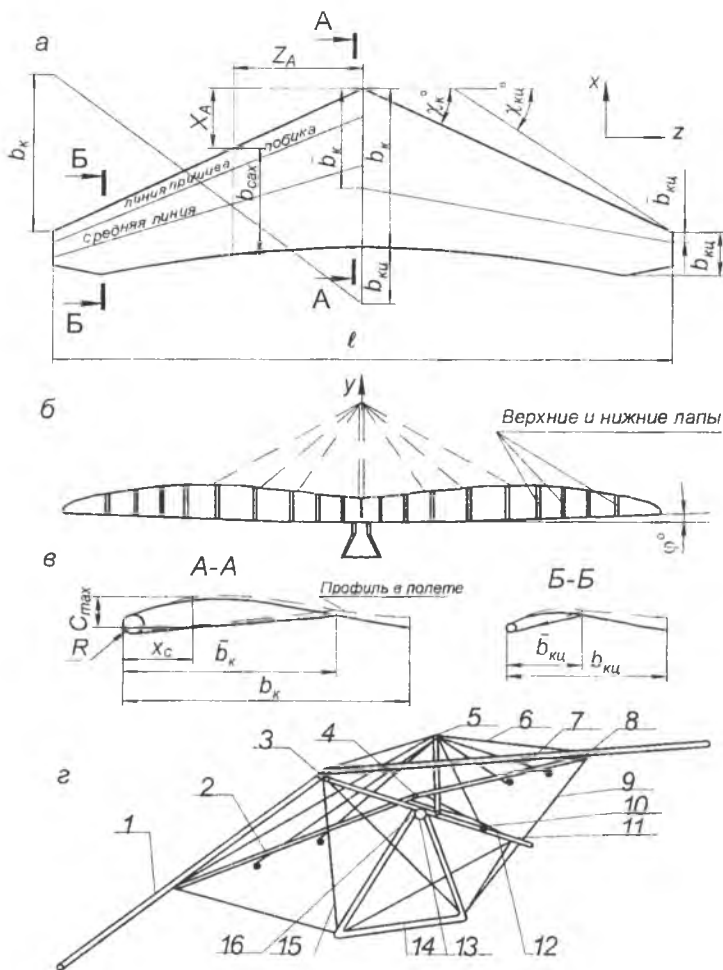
Параметры и конструкция крыла: а – вид в плане; б – вид спереди; в – профиль крыла; г – каркас крыла
